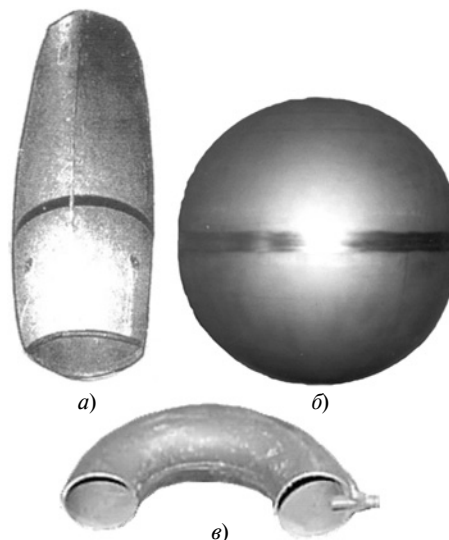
Изделия, полученные сваркой давлением:
